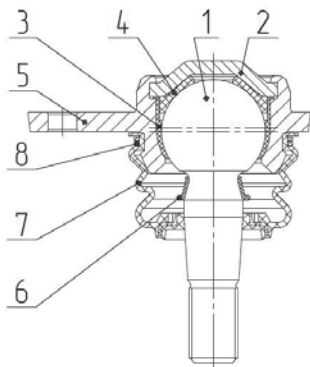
Шаровой шарнир 2123-2904192-03: 1 — шаровой палец; 2 — обойма вкладыша; 3 и 4 — части вкладыша, охватывающие экваториальную и полярную части головки; 5 — корпус; 6 — распорная втулка; 7 — чехол защитный; 8 — пружинное кольцо
